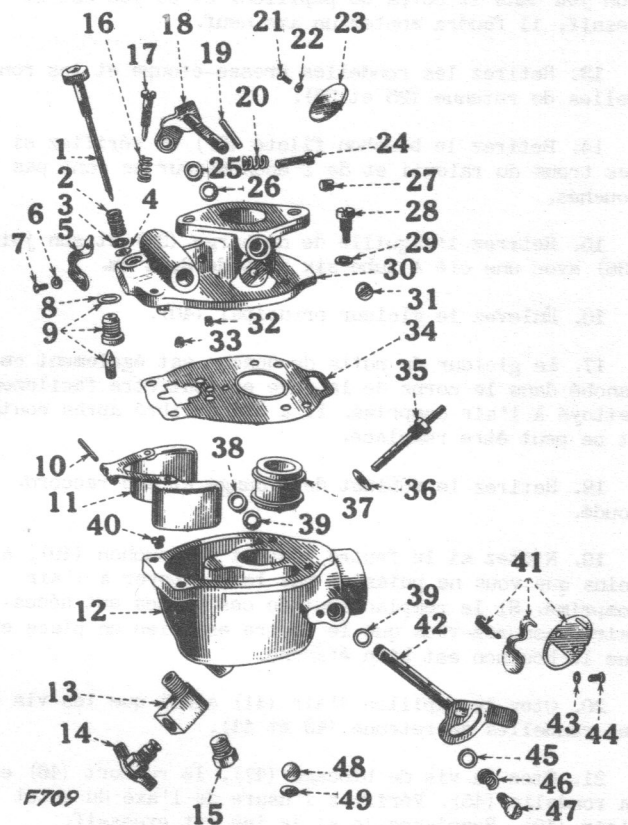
Vue éclatée du carburateur Marvel-Schebler.
